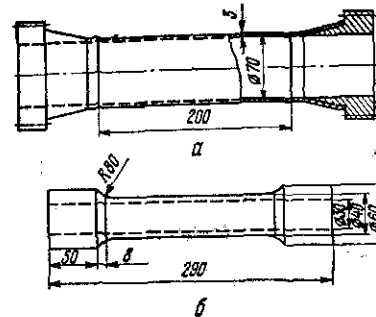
Трубчатые образцы для испытаний на кручение: а — тонкостенный [465]; б — толстостенный [274].
